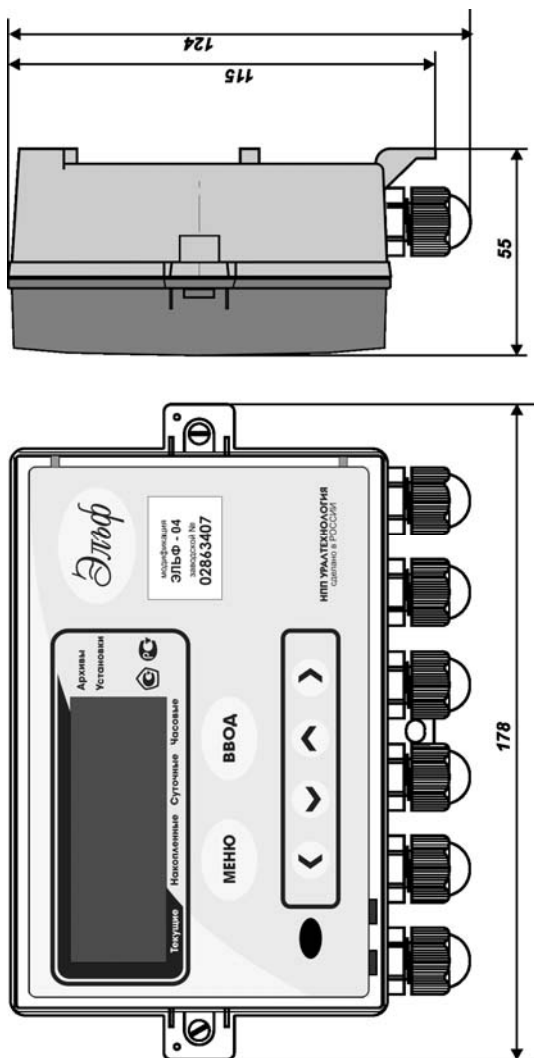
Габаритные размеры вычислителя Эльф
